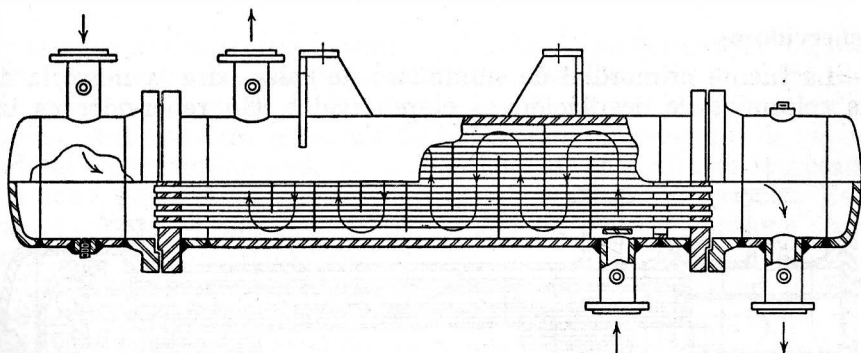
Cambiador uno-uno: carcasa de paso sencillo, tubos de paso sencillo, placa tubular fija. (Cortesía de Engineers and Fabricators, Inc.)
